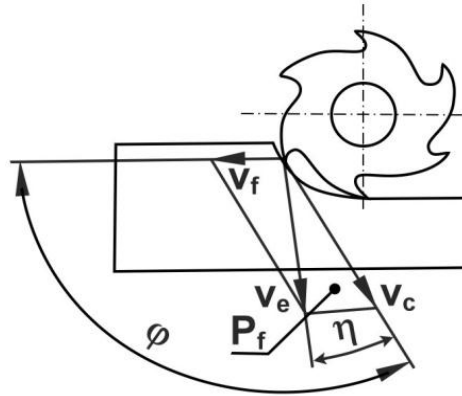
Protiběžné frézování podle ČSN ISO 3002/1
